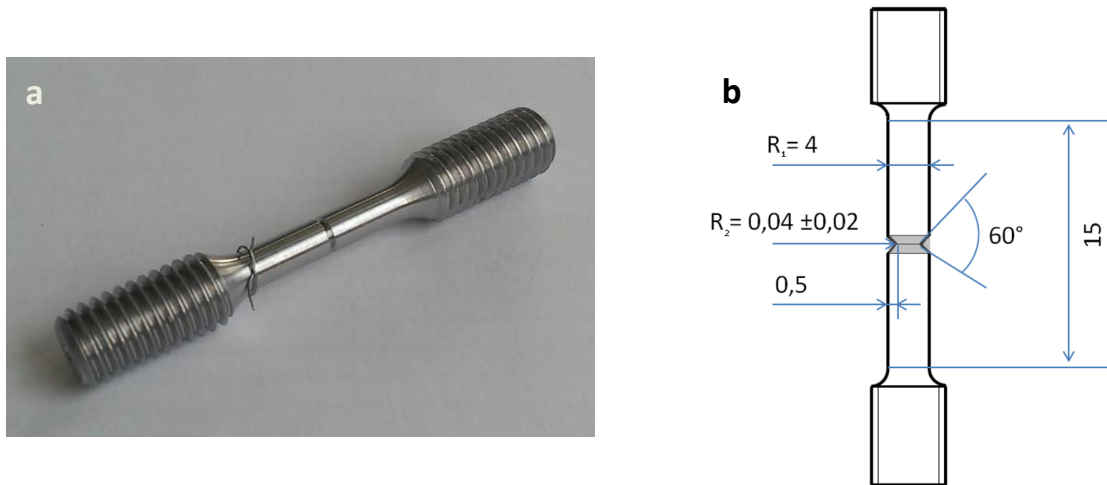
a) Photographie d'une éprouvette, b) schéma d'une éprouvette avec les dimensions de la zone utile en millimètres
